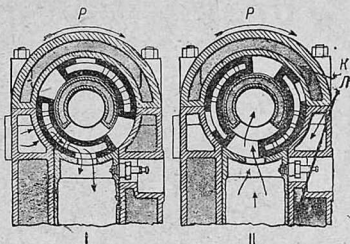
Схема впуска и выпуска горячей смеси в двигателе Пежо с клапанами Мак-Ларена
